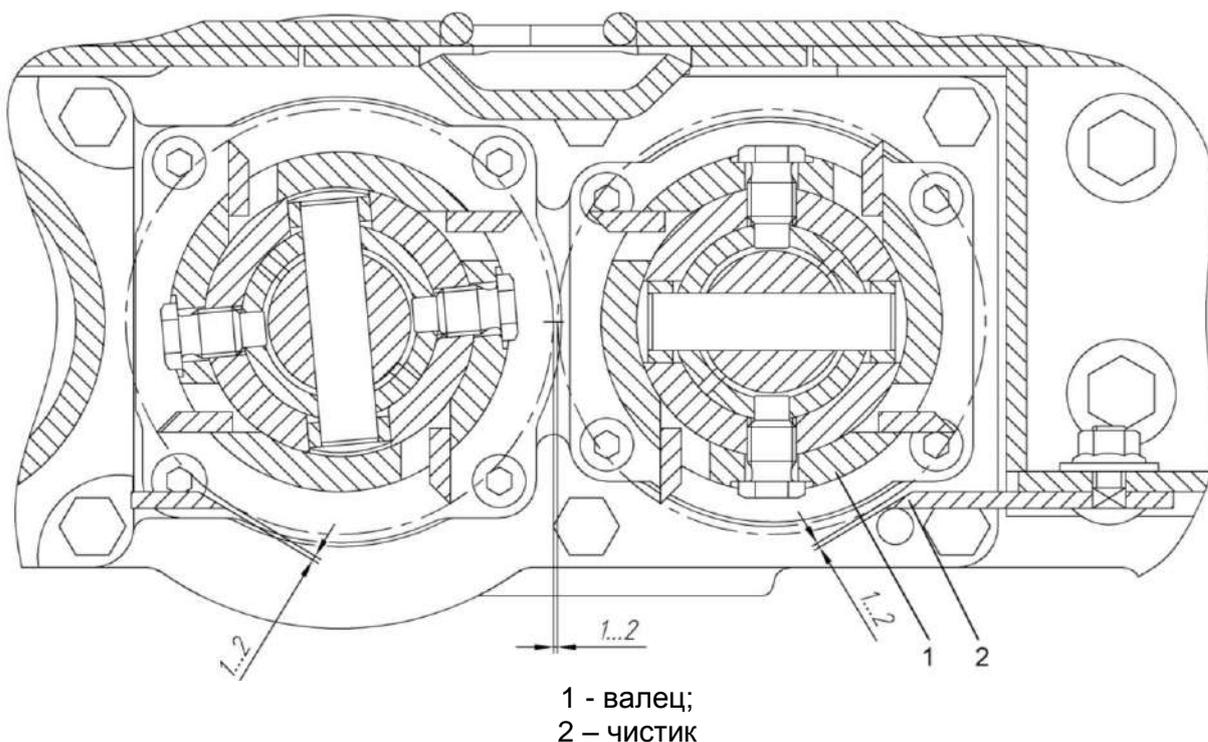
Регулировка бичей валцов и чистиков
